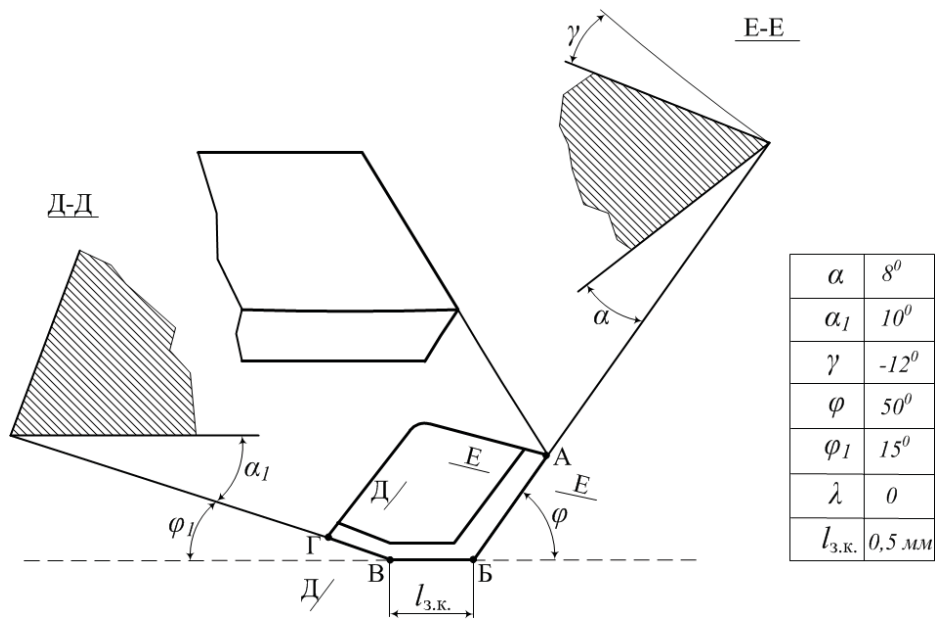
Геометрические параметры режущего зуба торцевой фрезы
